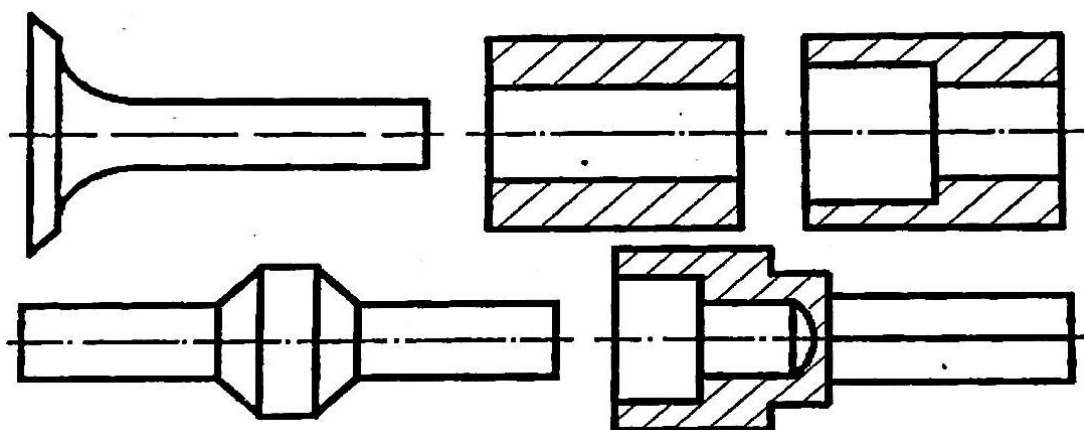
Формы заготовок при штамповке на ГКМ.
